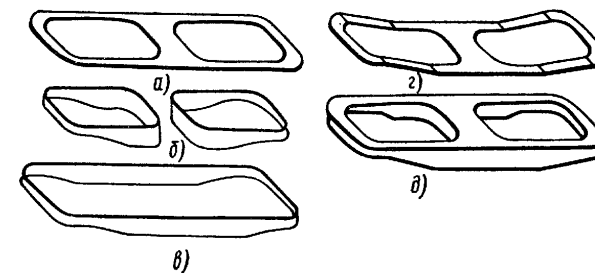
Последовательность сборочно-сварочных операций при изготовлении рамы
